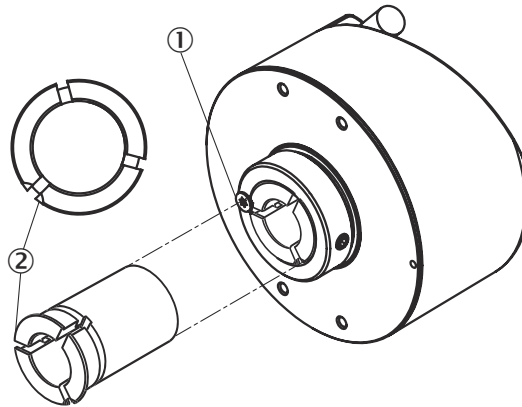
Montage Hülsen für Hohlwellenencoder
